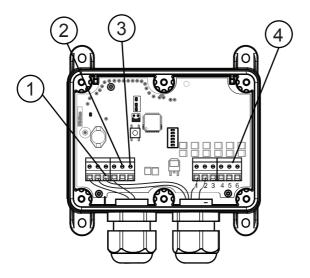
Sesam 800 RXM 12/24 V DC für Winde im Forstbetrieb ohne Kabel
